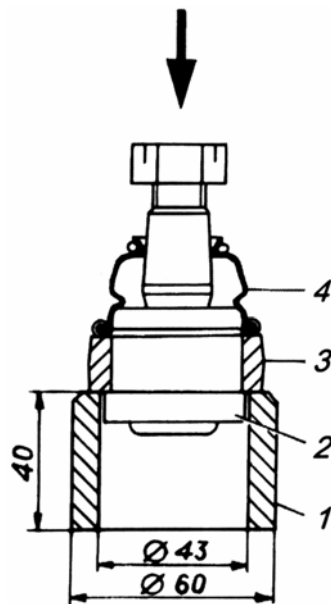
Выпрессовка шарнира рулевых тяг: 1 – втулка; 2 – шарнир; 3 – тяга или наконечник; 4 – защитный колпак
